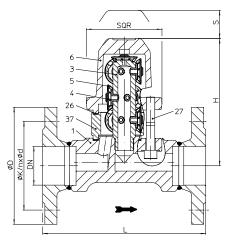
1....10K2 (DN40-50) mit 10 Kapseln, mit Flanschen
